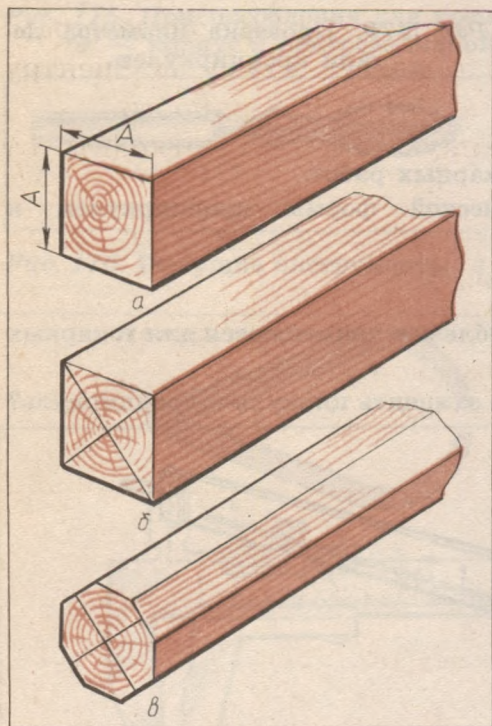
Обработка заготовки вручную для токарных работ: а — в — последовательность работы.
